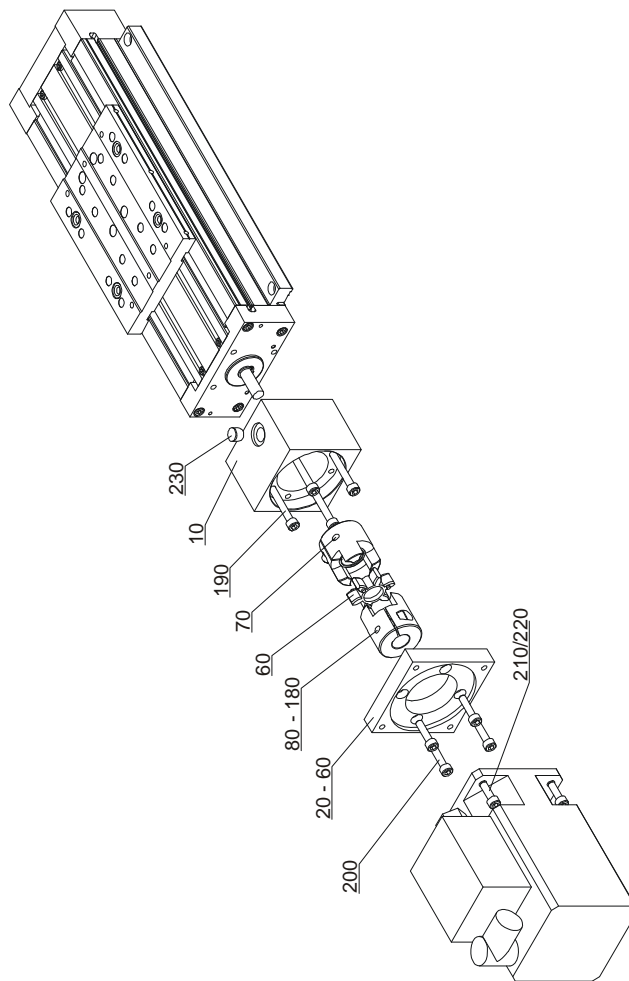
Explosion axialer Motorflansch (TG 1000691)
